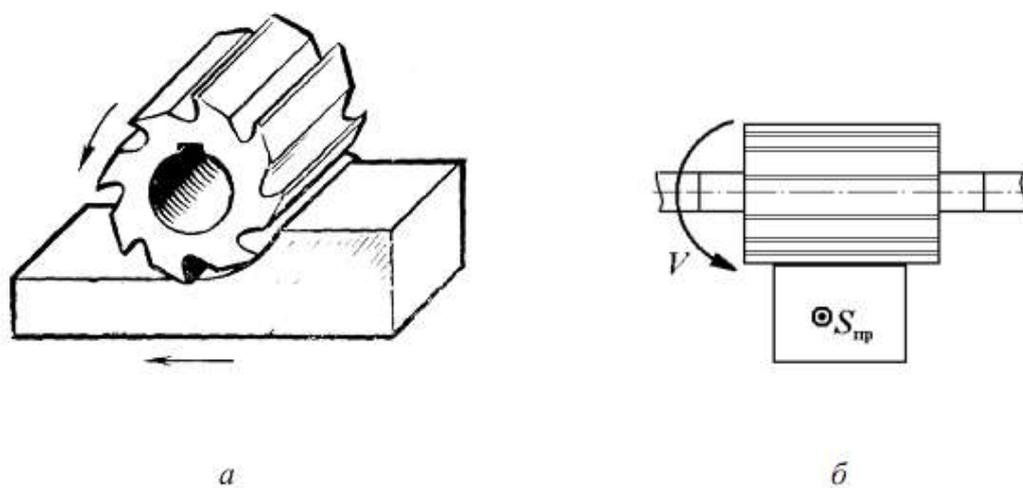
Обработка плоскостей цилиндрической фрезой
